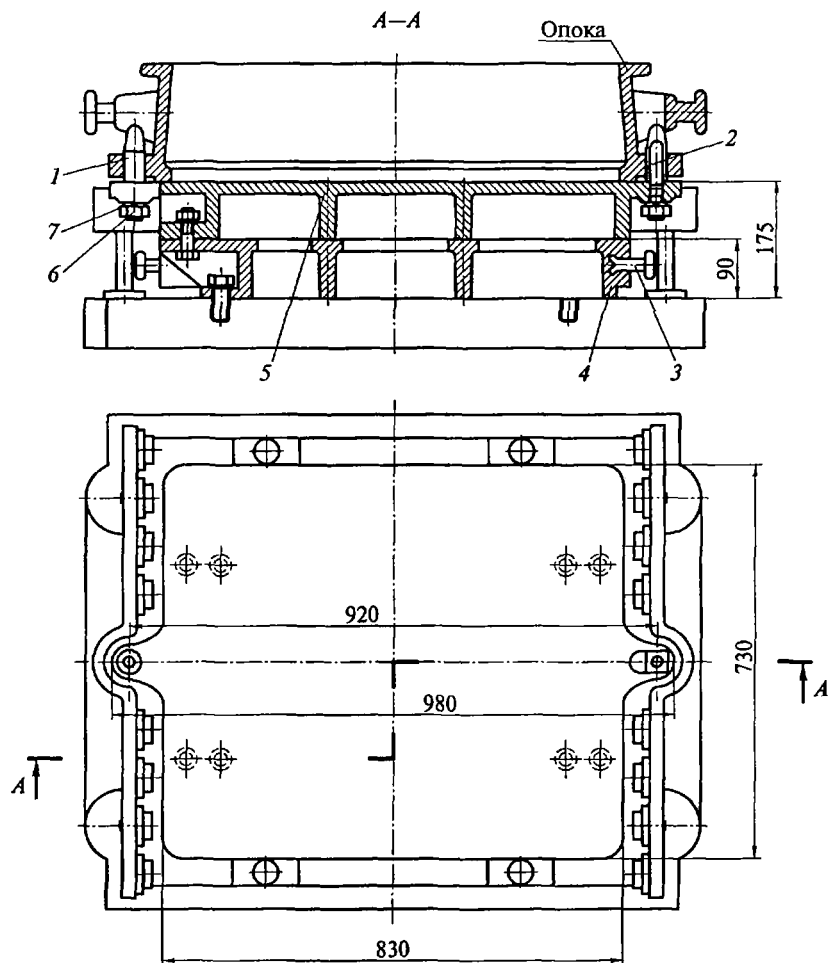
Сборочный чертеж крепежа модельной плиты с опокой на столе формовочной машины:
